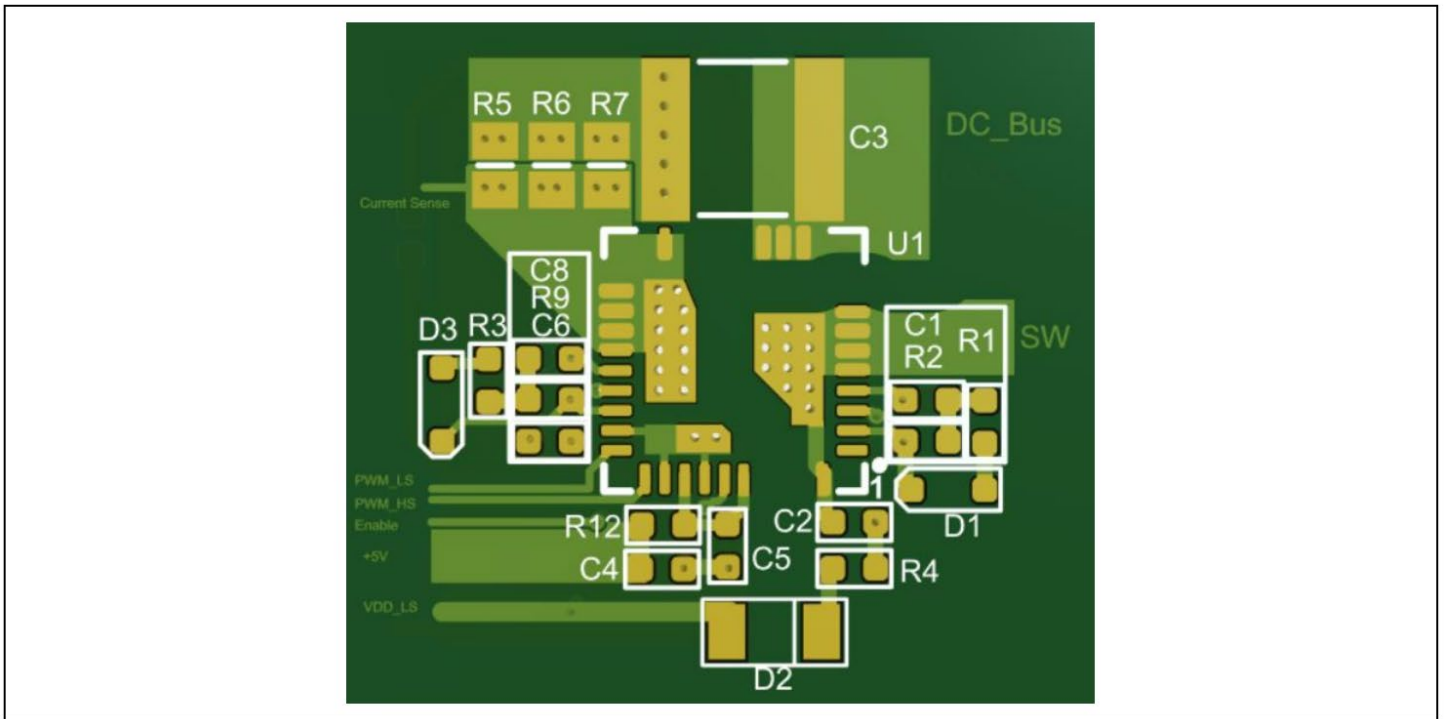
CoolGaN™ IPS 外部元件在 PCB 上的放置
